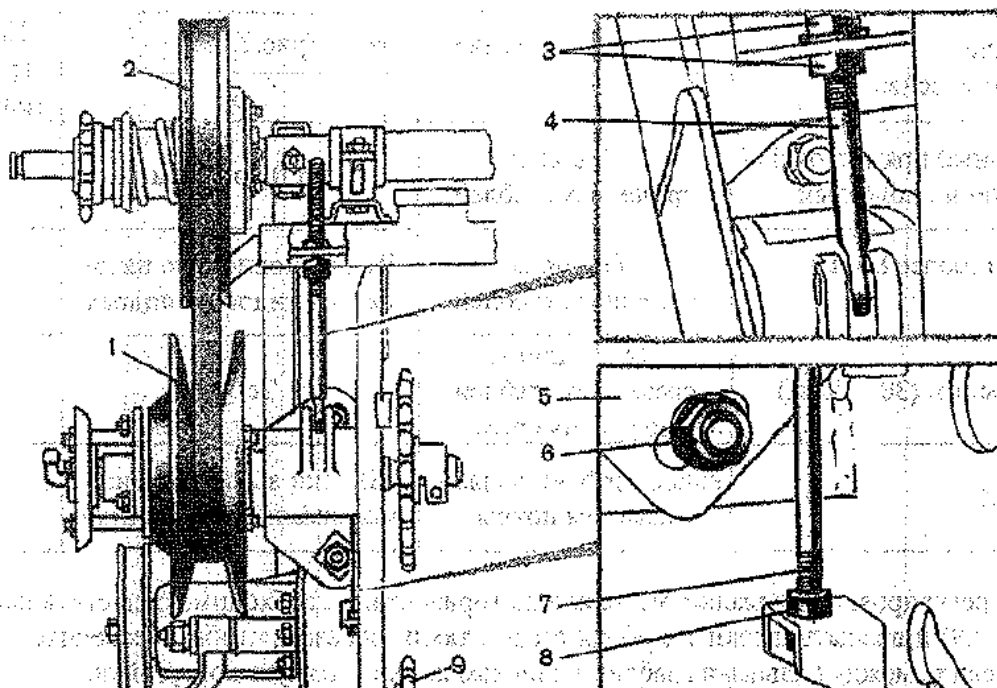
Вариатор жатки: 1-шків ведучий; 2-шків ведомий; 3,8-гайки; 4,7-винты; 5-пята; 6-болт; 9-звездочка
